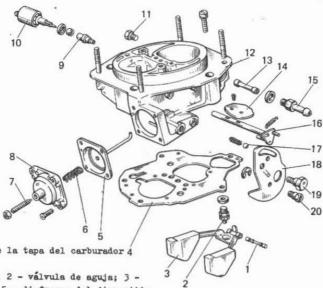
Piezas de la tapa del carburador 4 21053-1107010:
